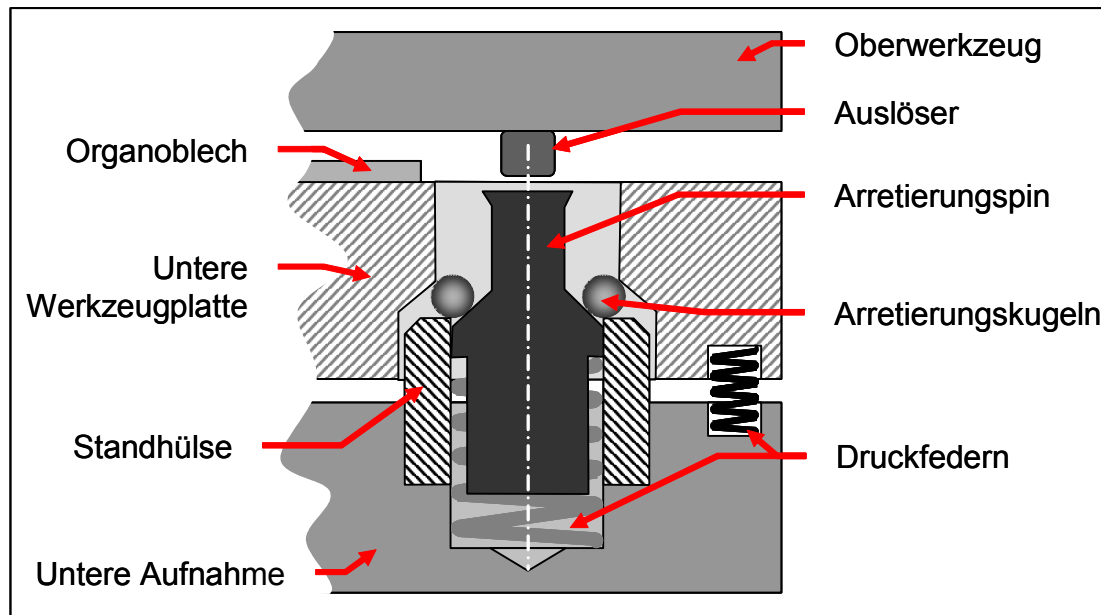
Detailansicht des Auslösemechanismus der unteren Werkzeugplatte
